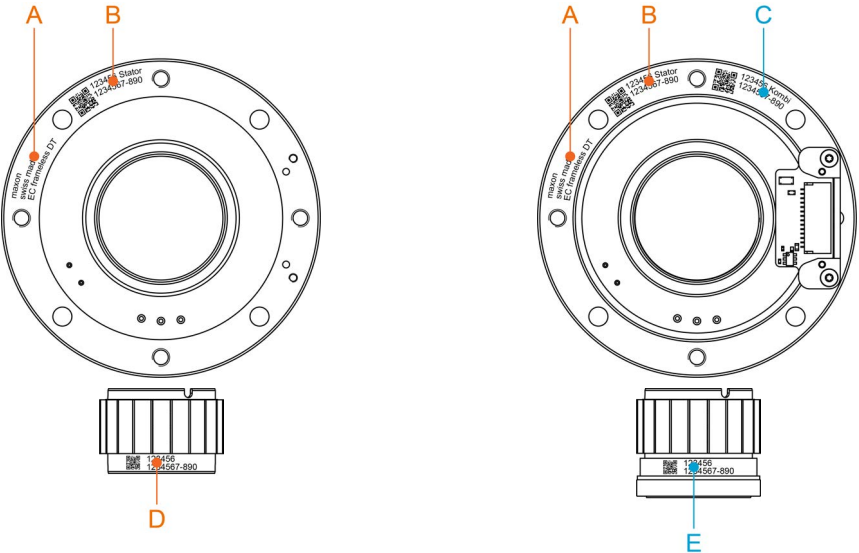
Typenschild (typisch) – EC frameless DT ohne (links) und mit TSX MAG Encoder (rechts)
